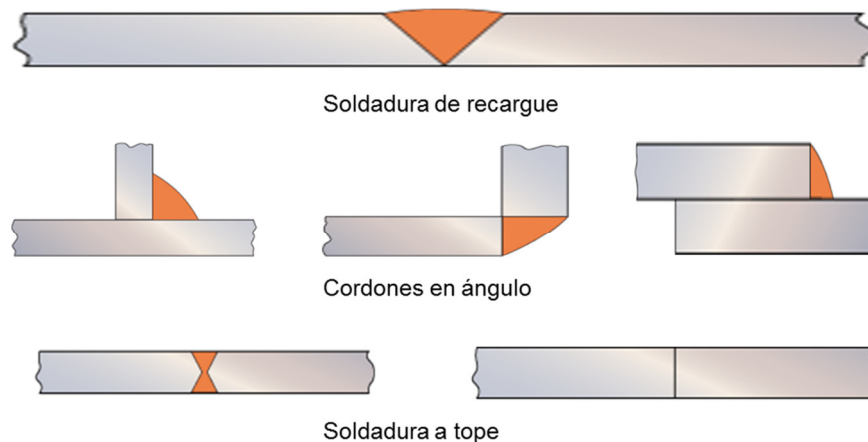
Representación esquemática de los tipos de soldaduras.
